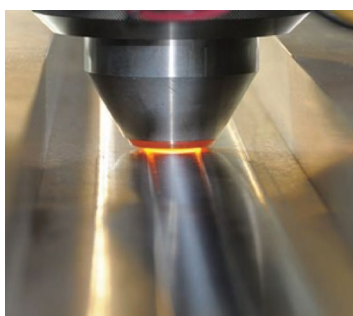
Сварка трением с перемешиванием алюминиевых сплавов
